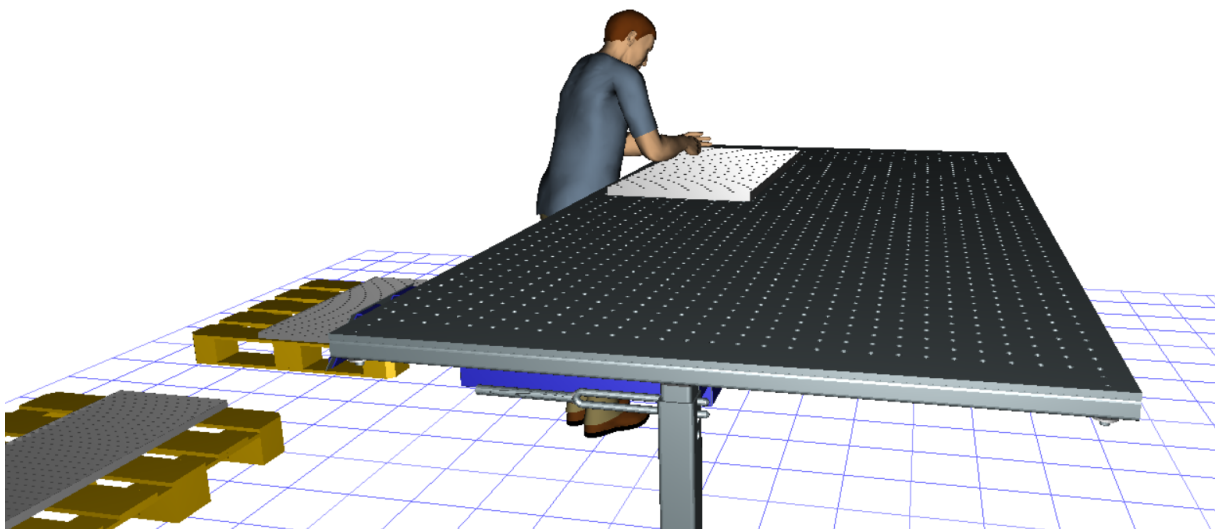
Výkres sestavy interně konstruovaného stolu [Interní archiv]
